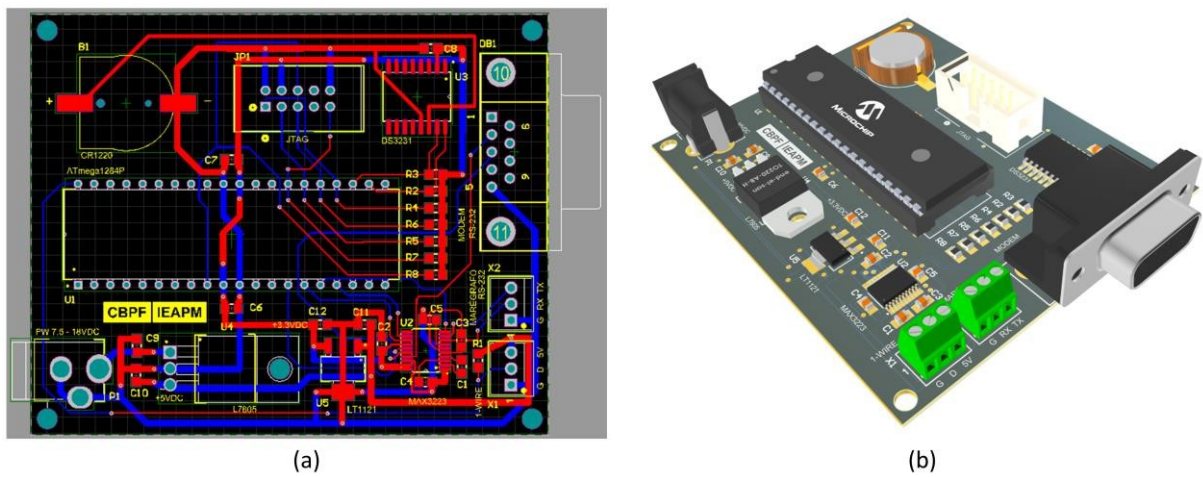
Modelo do circuito para a fabricação da PCB (a) e simulação 3D apresentando a PCB em perspectiva.
